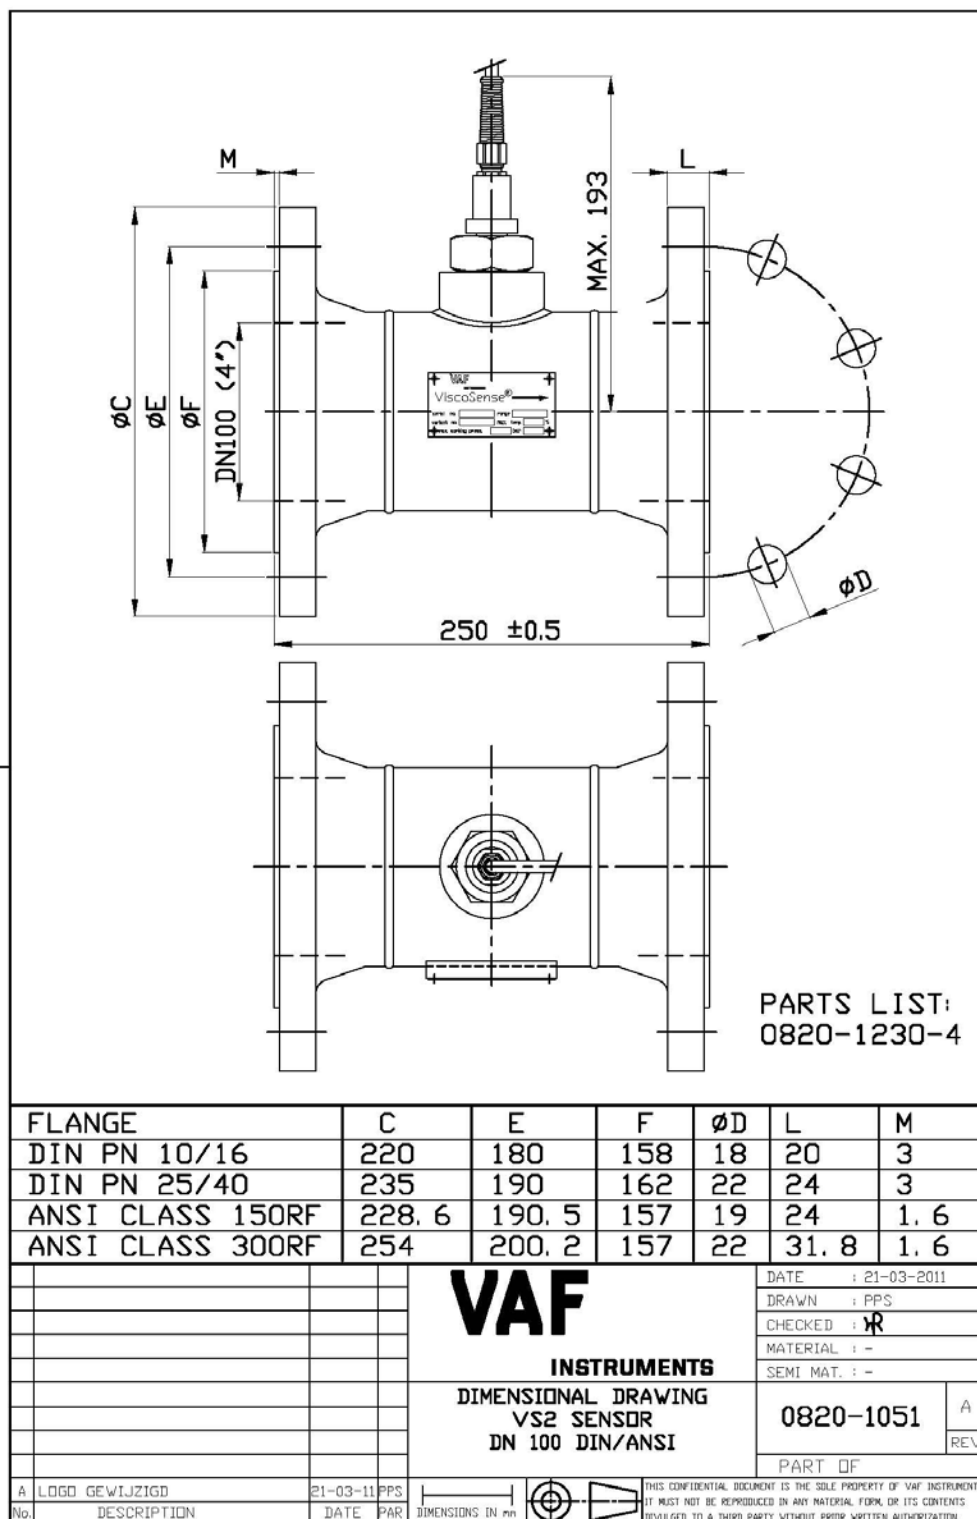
Dimensioni del sensore ViscoSense®2 (Tutte le dimensioni sono in millimetri).
